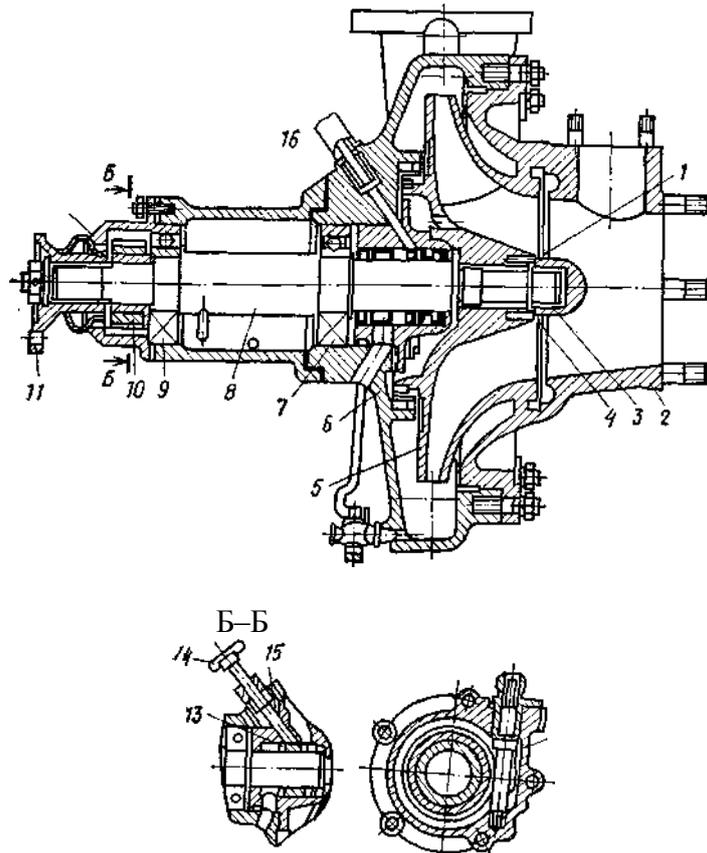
ПН-40УА (продольный разрез): 1 – шпонки; 2 – крышка; 3 – гайка; 4 – стопорная шайба; 5 – рабочее колесо; 6 – корпус; 7, 9 – подшипники; 8 – вал; 10 – червячный привод тахометра; 11 – муфта-фланец; 12 – манжета; 13 – уплотнительный стакан; 14 – винт; 15 – пластиковая набивка; 16 – шланг
